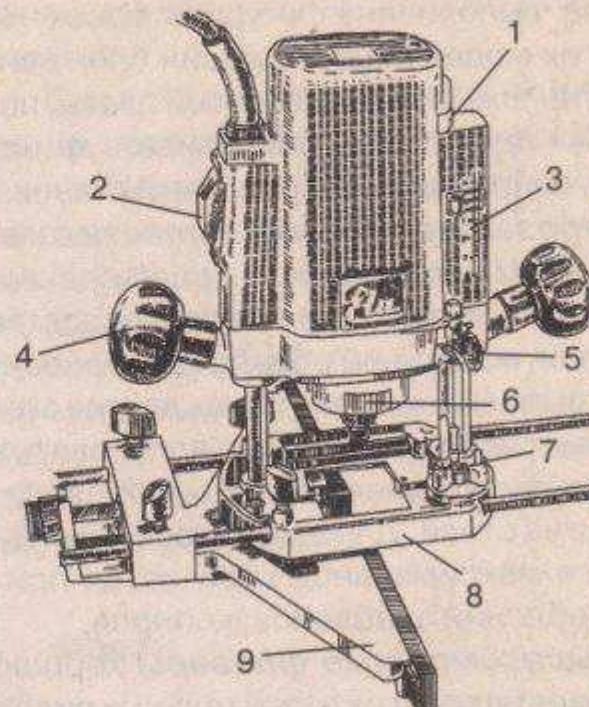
Ручная фрезеровальная машина: 1 — регулятор скорости; 2 — выключатель; 3 — ограничитель глубины; 4 — ручка; 5 — фиксатор механизма вертикальной подачи; 6 — замок шпинделя; 7 — турельный стопор; 8 — базовая плата; 9 — боковая линейка
